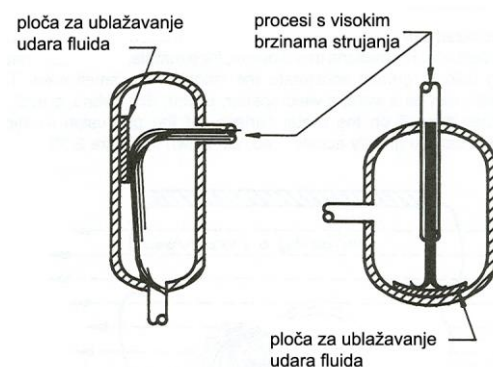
Sprečavanje pojave erozijske korozije osiguravanjem pravilnog strujanja [1].
